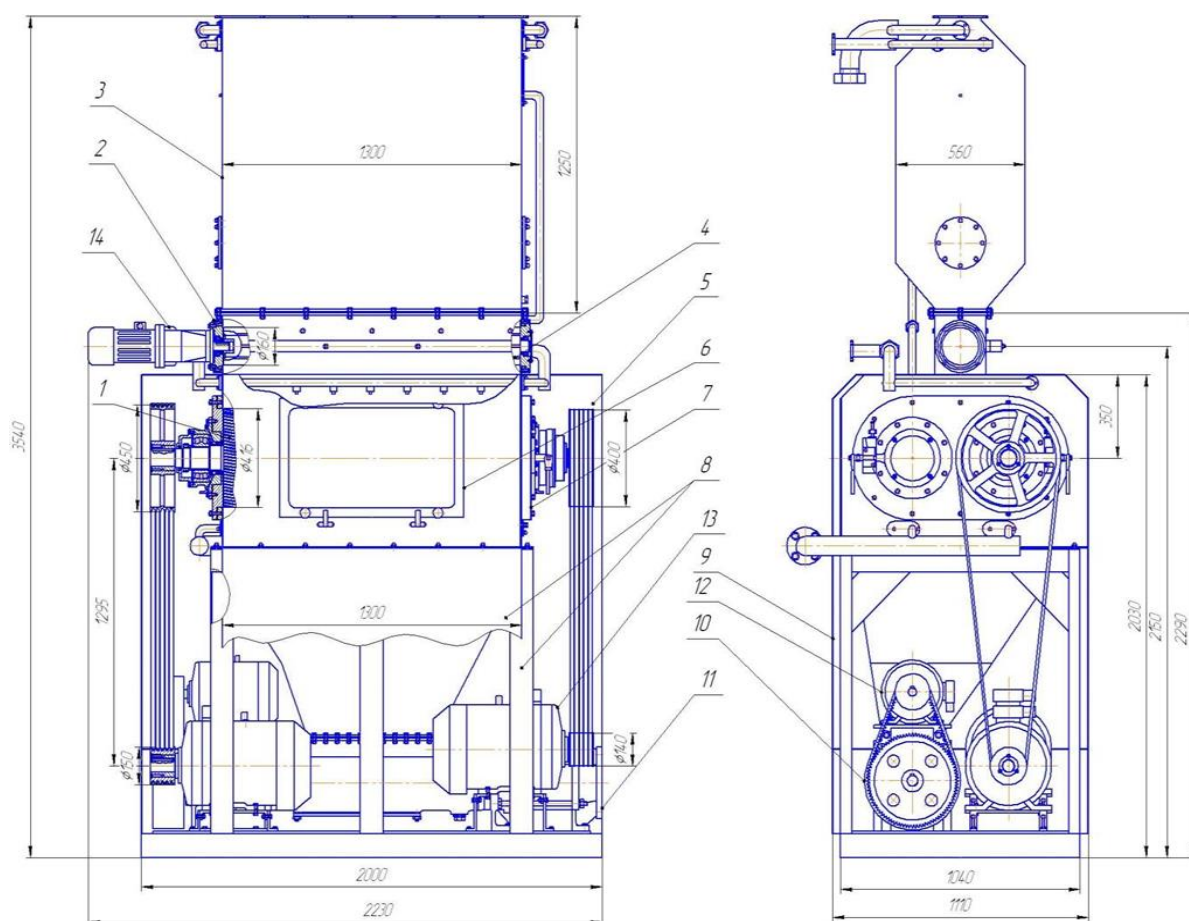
Конструкція дробарки «MILLSTAR»
